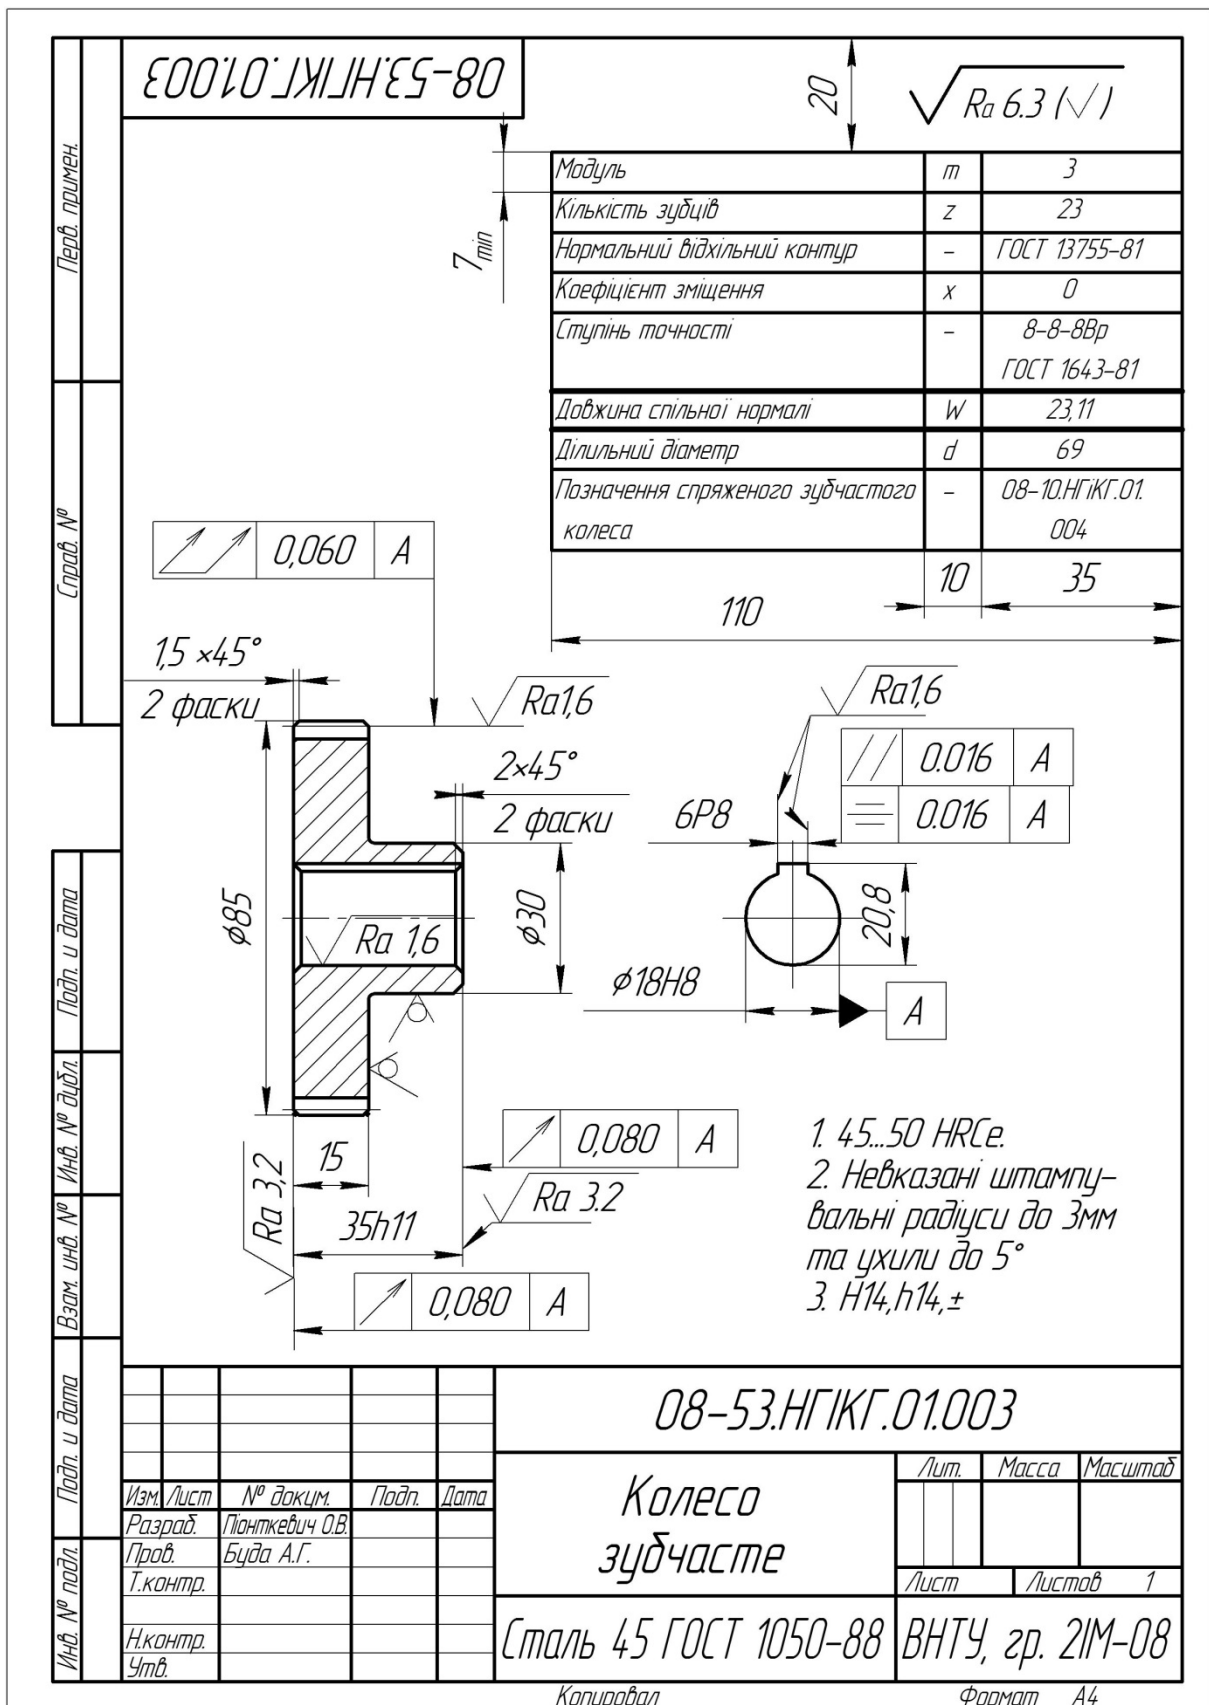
Робочий кресленник прямозубого некоригованого циліндричного зубчастого колеса
